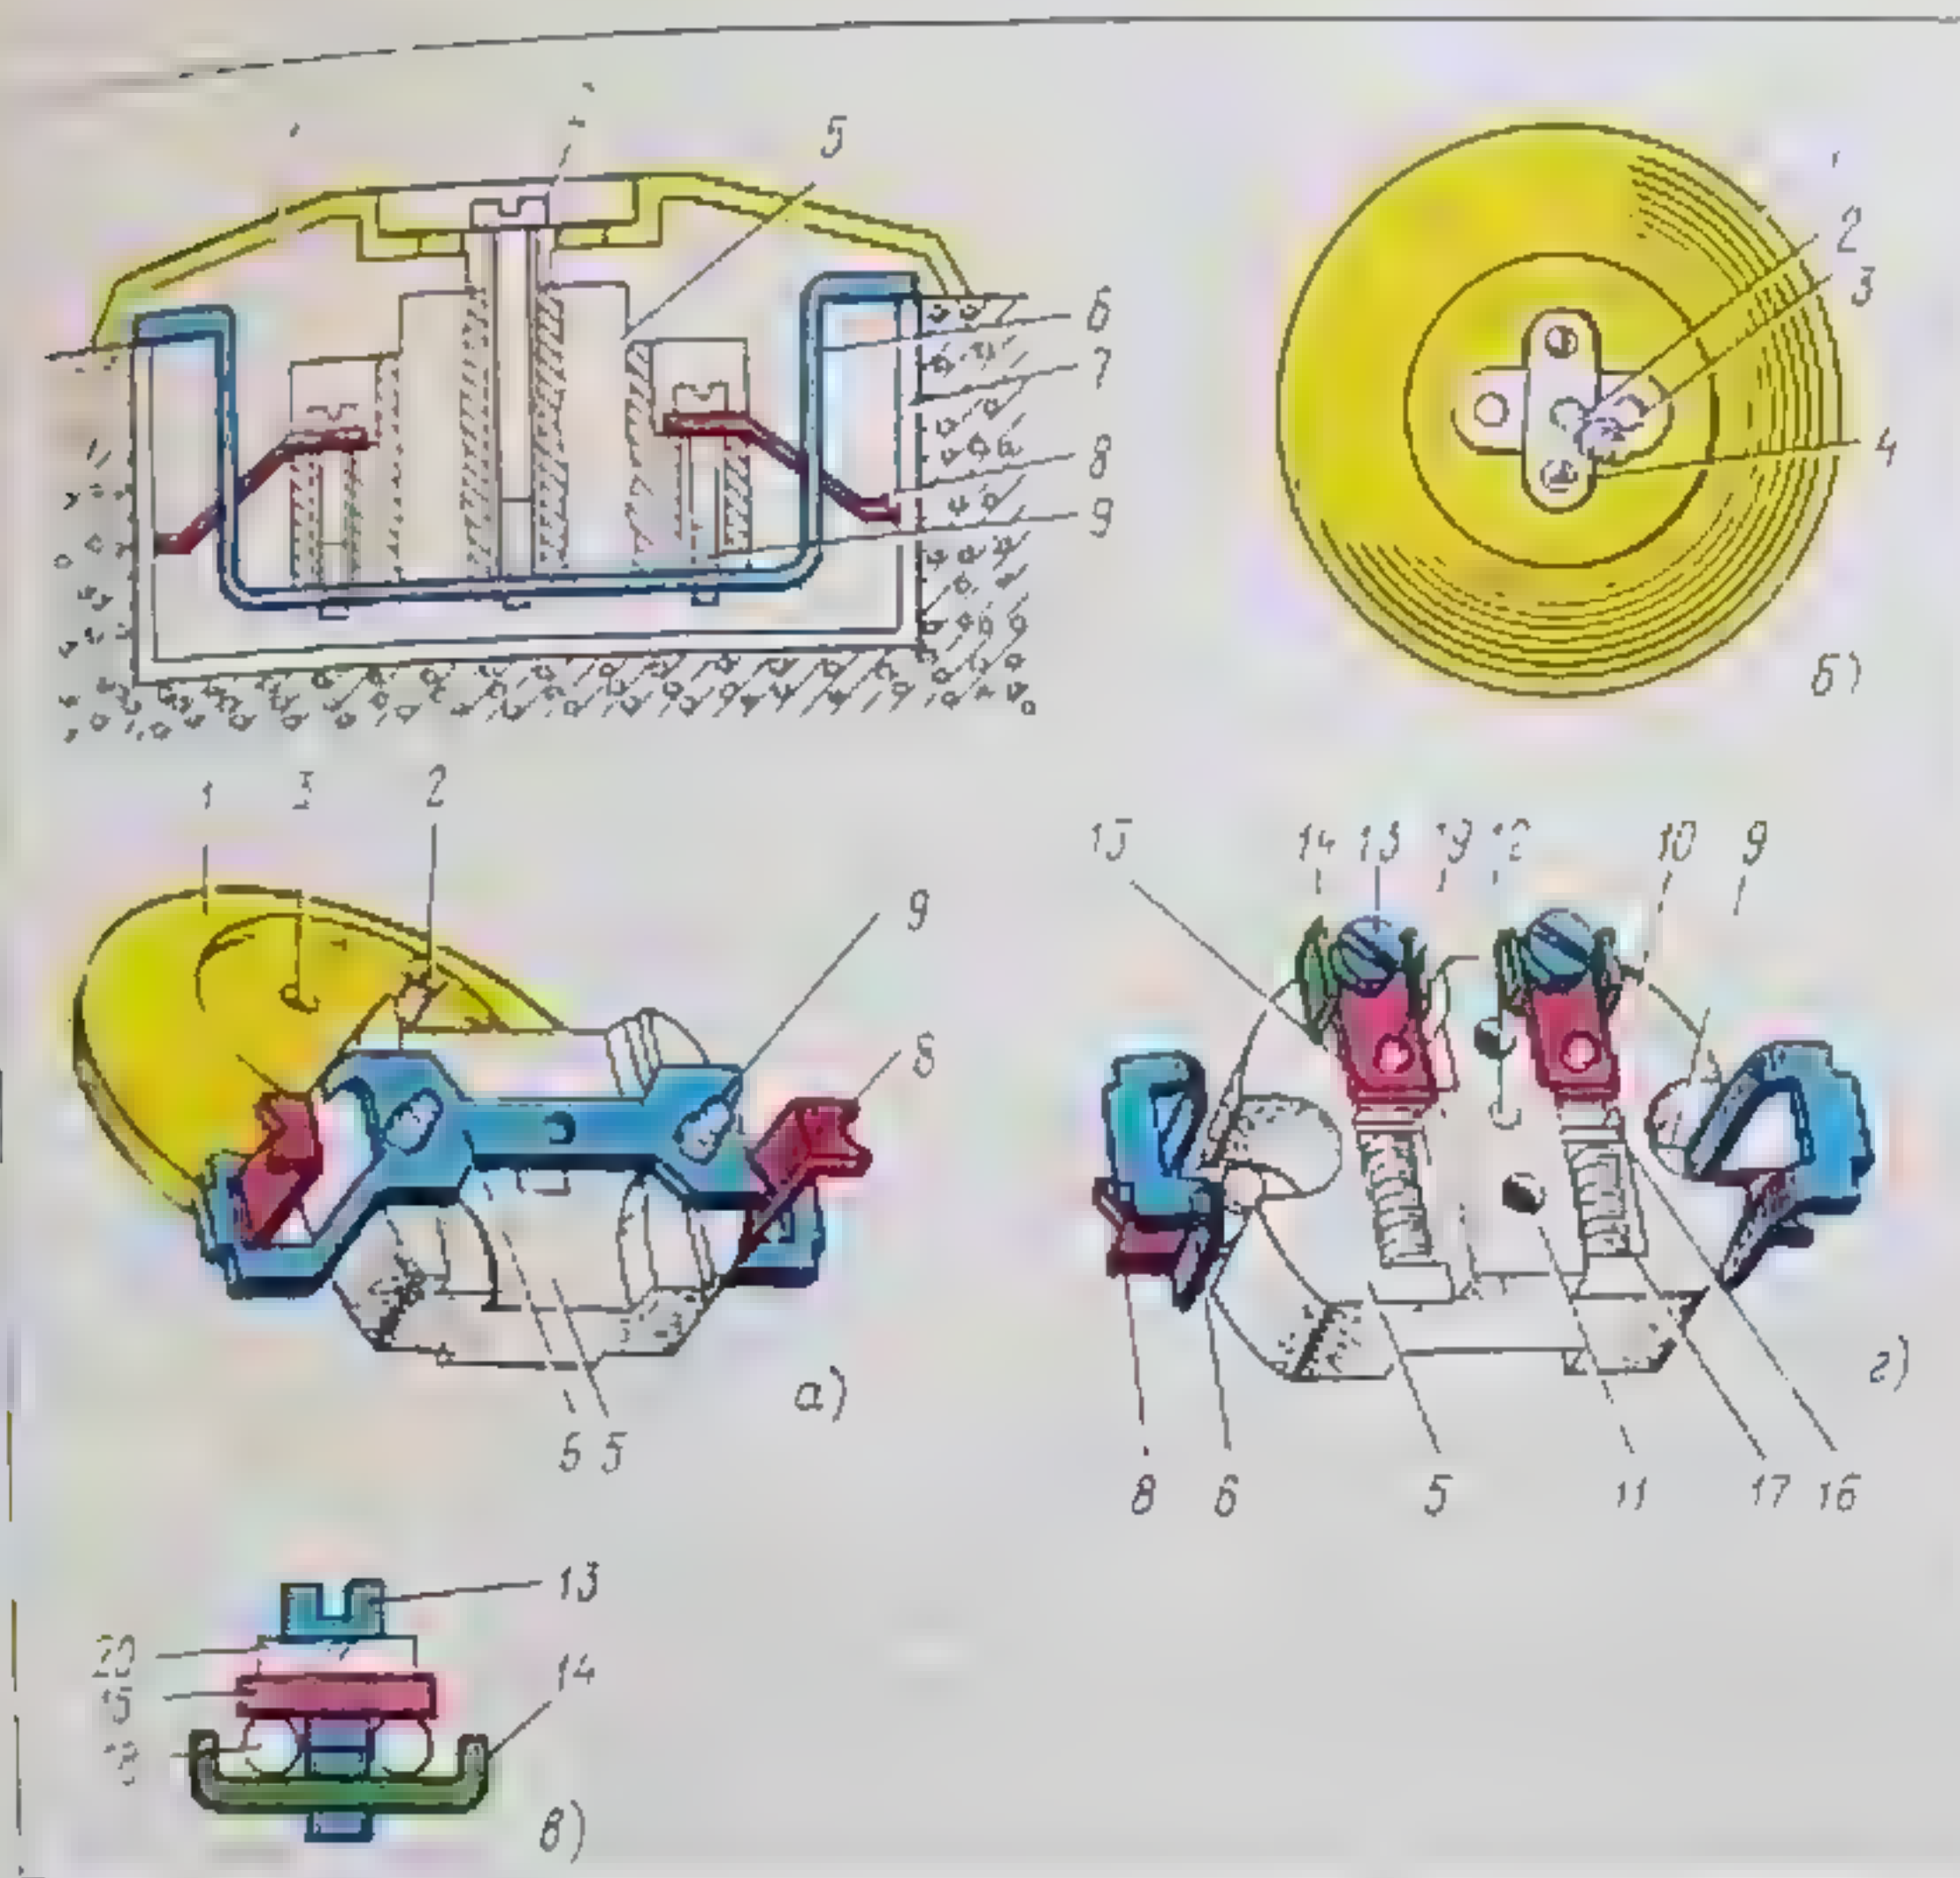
Штепсельная розетка для скрытой установки без защитного контакта
